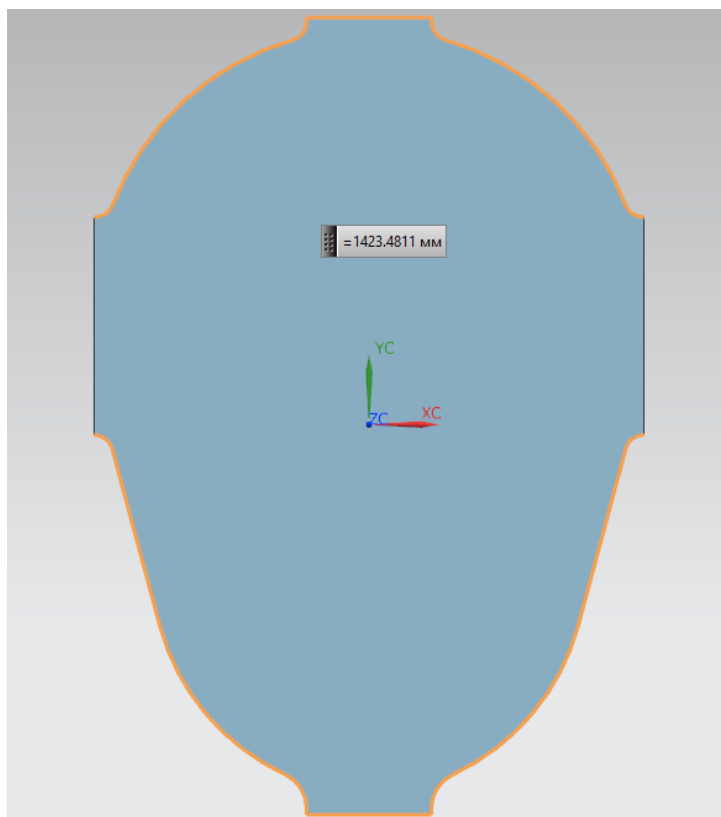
Длина линии реза предлагаемой заготовки
